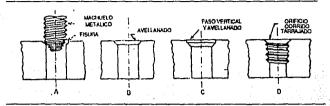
Abocardado recomendado para rocas machueladas. (Ref. 2).
